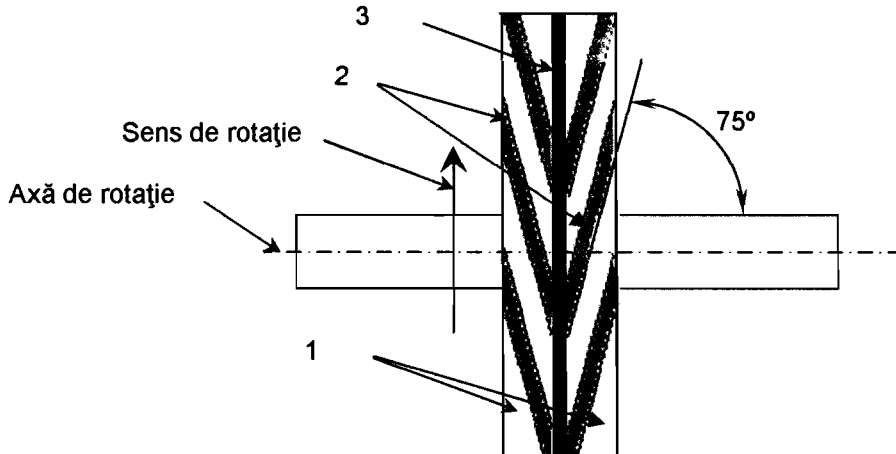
Element rotoric cu două rotoare, cu magneți dispuși sub un unghi de 75° față de axa de rotație, iar magneții de pe cele două rotoare dispuși simetric față de discul de oțel, în formă de V, cu deschiderea spre sensul de rotație
